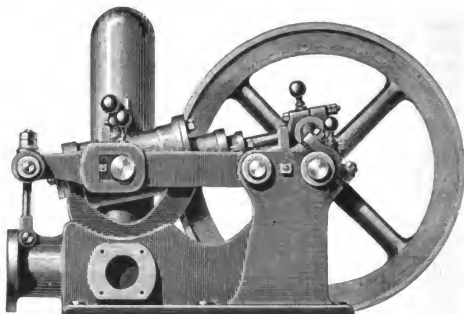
Schmid's Wasserdruckmotor. Aussenansicht.
